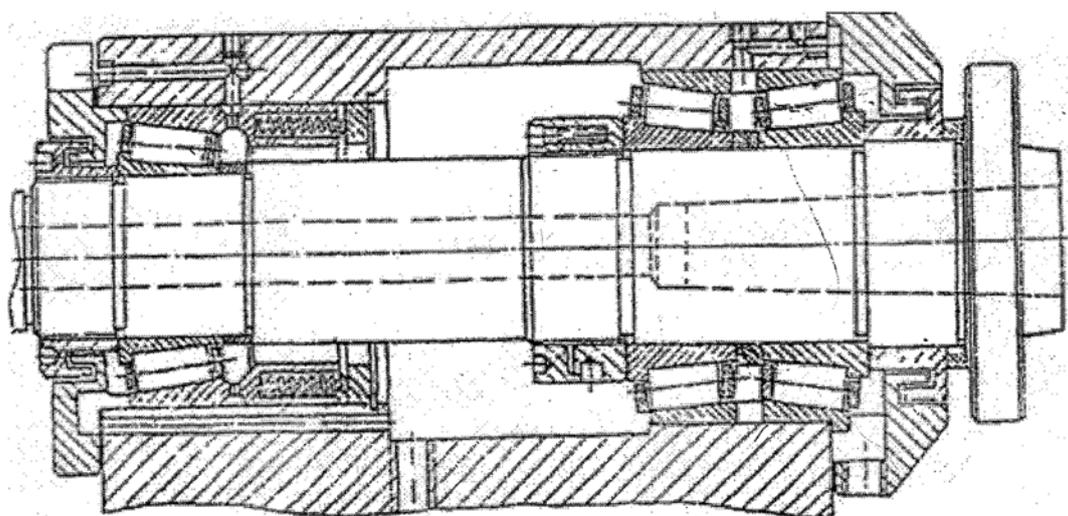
Шпиндельный узел станка с ЧПУ на роликоподшипнике с упорным бортом типа 697000 в передней опоре и однорядном роликоподшипнике типа 17000 с предварительным натягом пружинами в задней опоре
